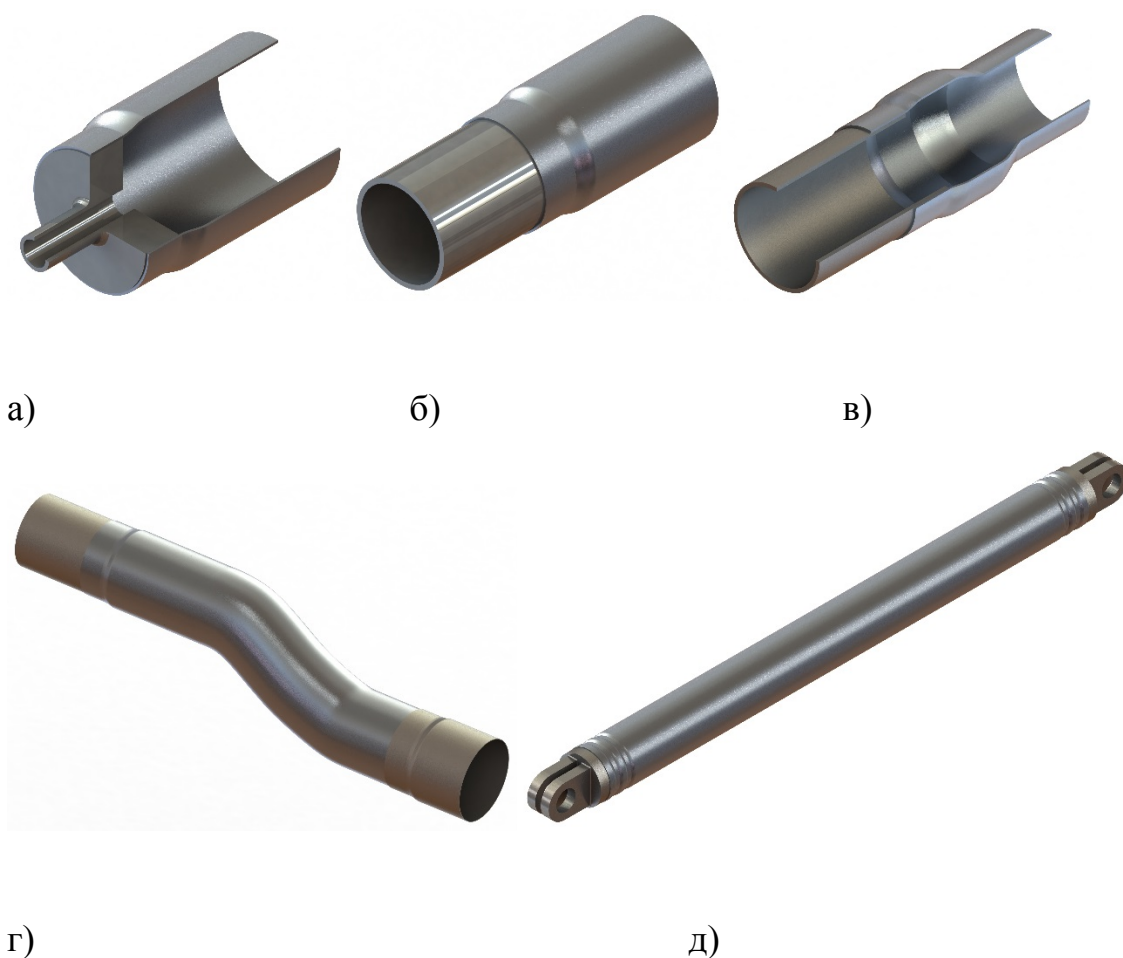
Общий вид неразъёмных трубчатых соединений:
